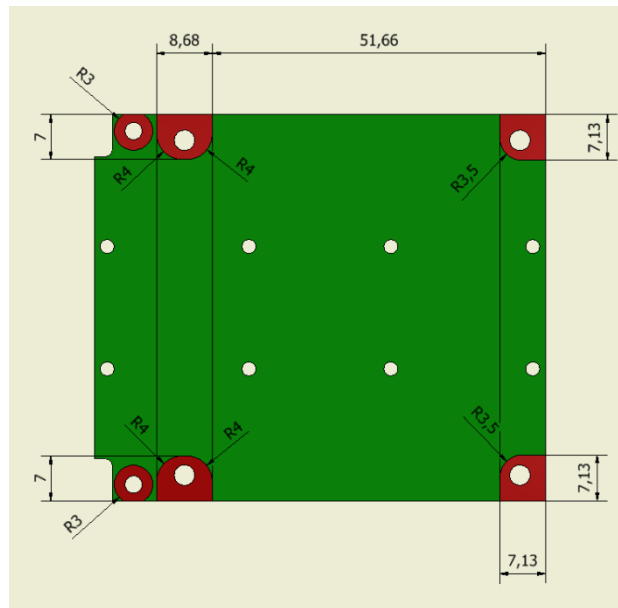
Aree di rispetto lato BOTTOM del PCB.
